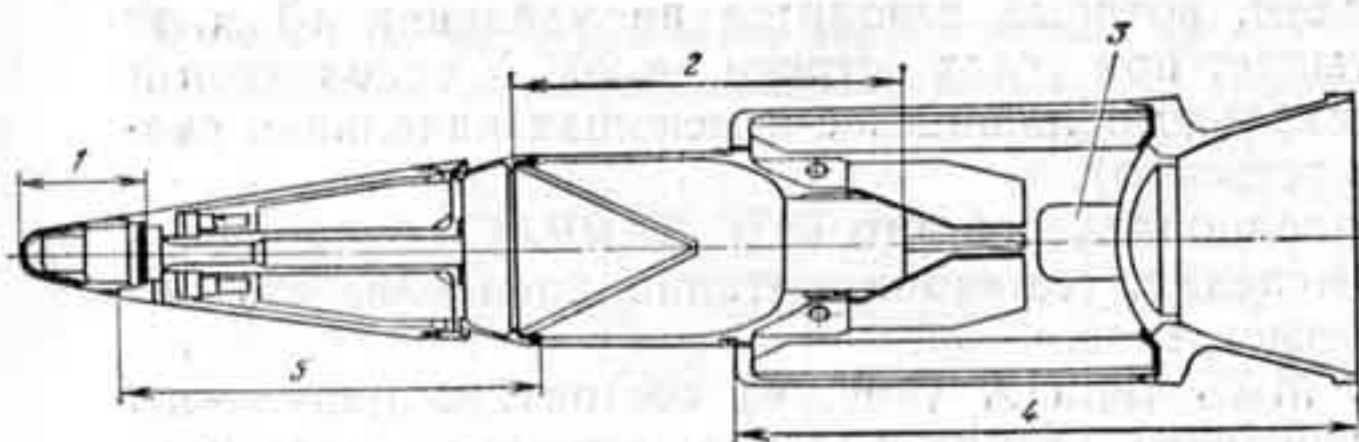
80-мм противотанковая граната и РПГ АСЛ/АРХ 80 (общий вид и продольный разрез): 1 — пьезоэлектрический генератор; 2 — боевая часть; 3 — воспламенитель; 4 — стартовый реактивный двигатель; 5 — маршевый реактивный двигатель
